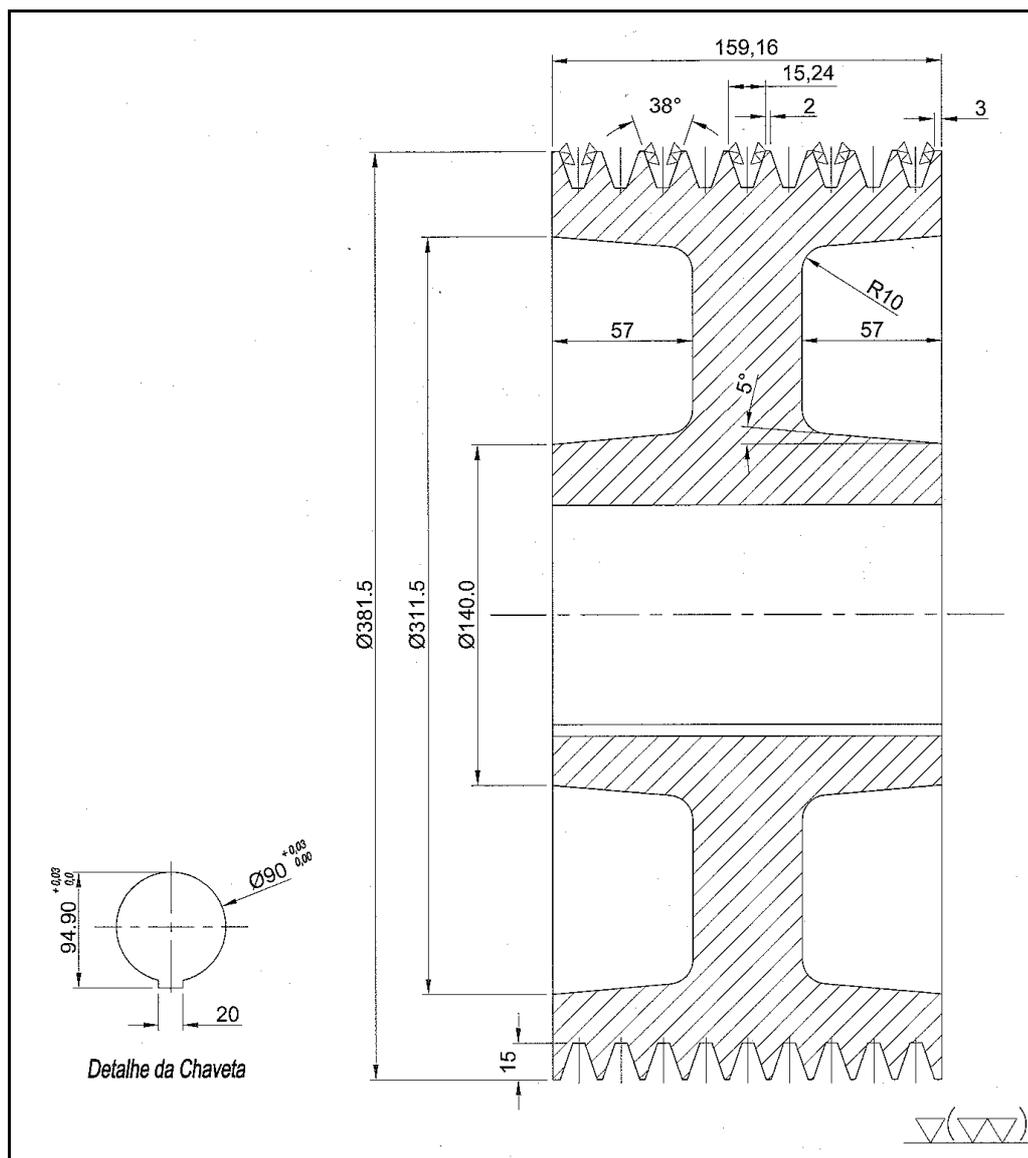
Desenho técnico realizado com auxílio do software Auto-Cad.
